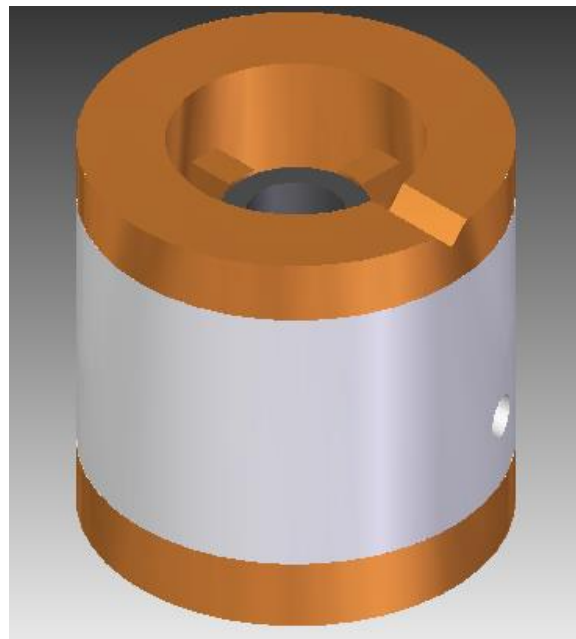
CAD del Conjunto partes internas del horno. Fuente: Autor
